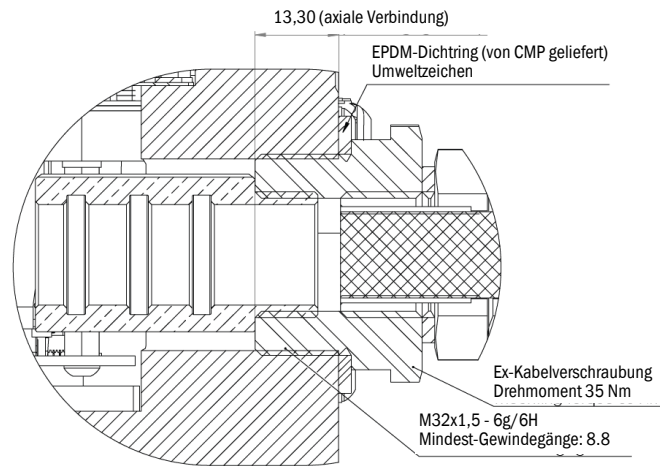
Verschraubter Flammweg zwischen Ex-Kabelverschraubung und Ex-Gehäusekörper
